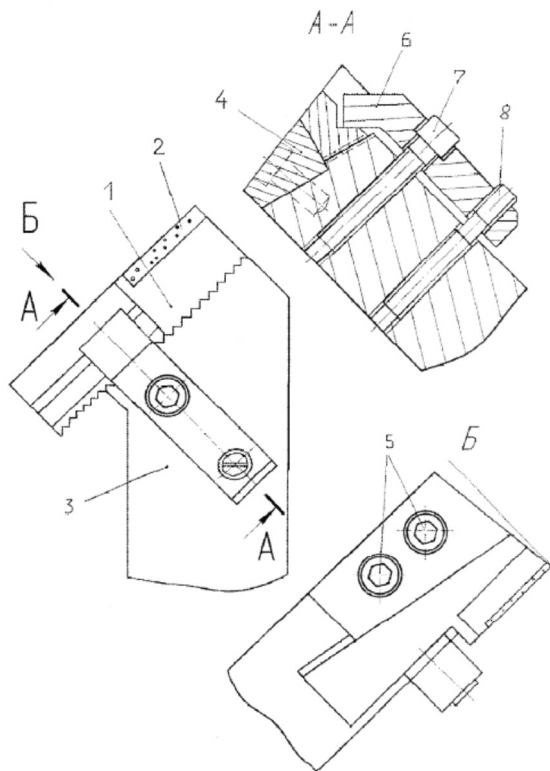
Сборный проходной резец с разрезом А-А и видом Б:
